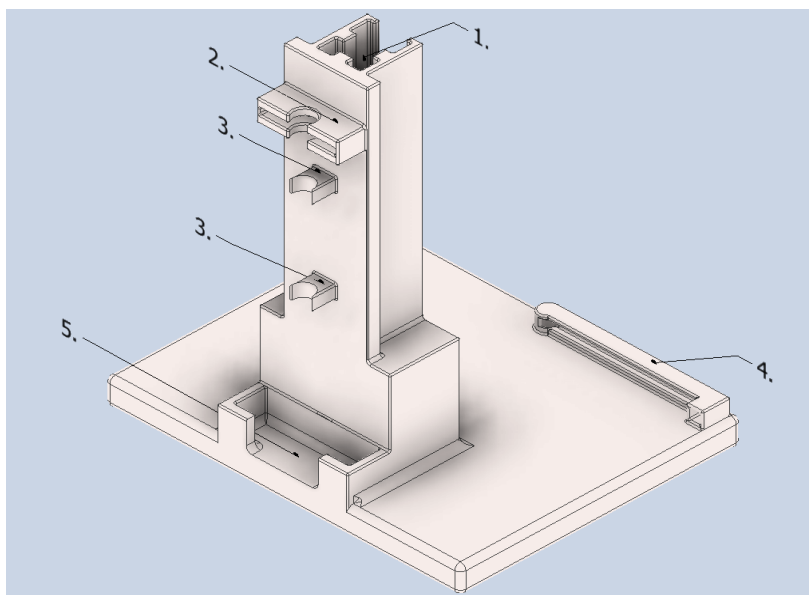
Soporte principal de la estructura mecánica diseñado en Inventor [5].
